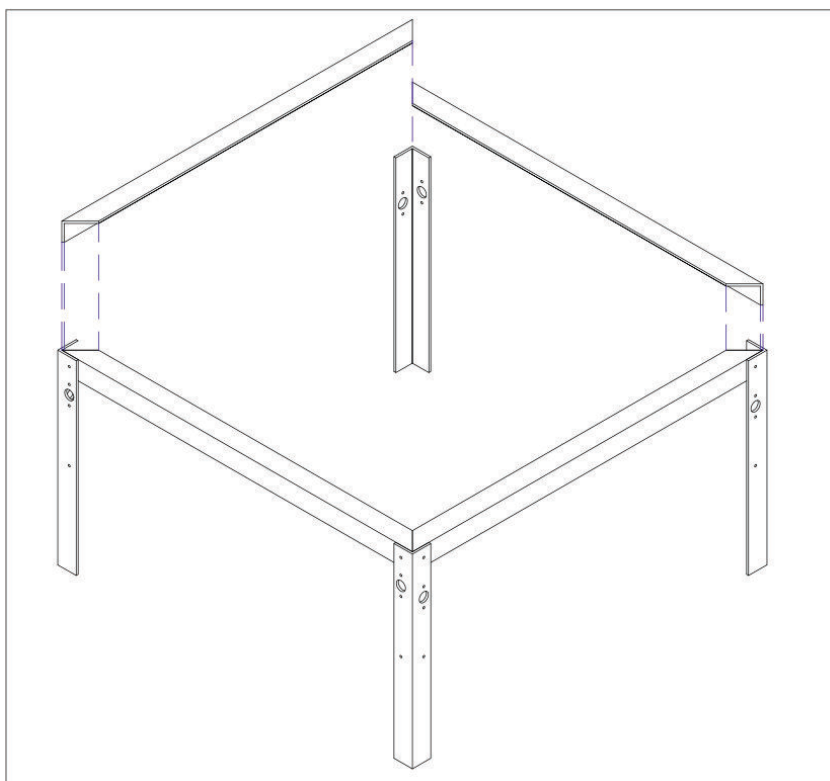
Esquema del procedimiento de montaje de los perfiles horizontales superiores de la estructura.
